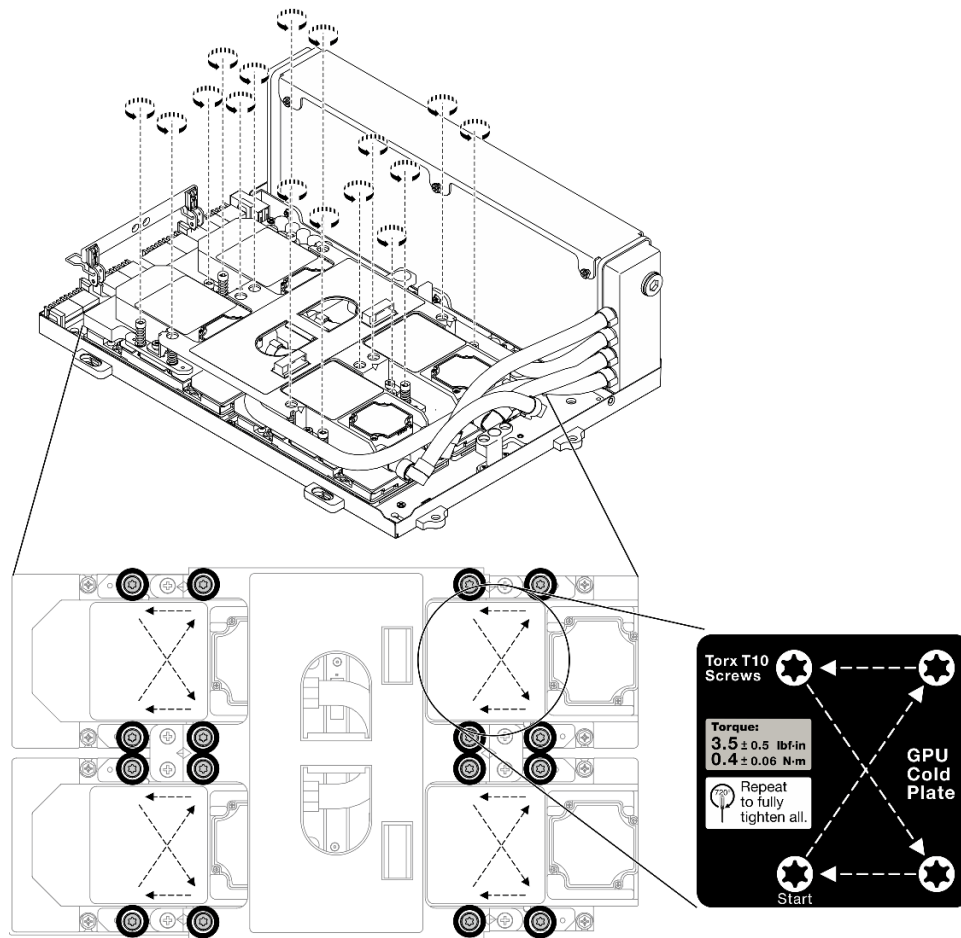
Lösen der Schrauben auf den Kühlplatten
